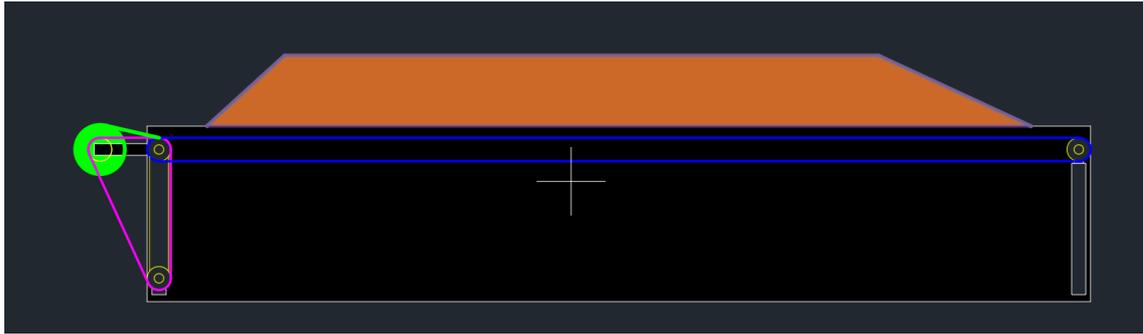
Sistema eje-correa con lona enrollada y cilindros bajados.
